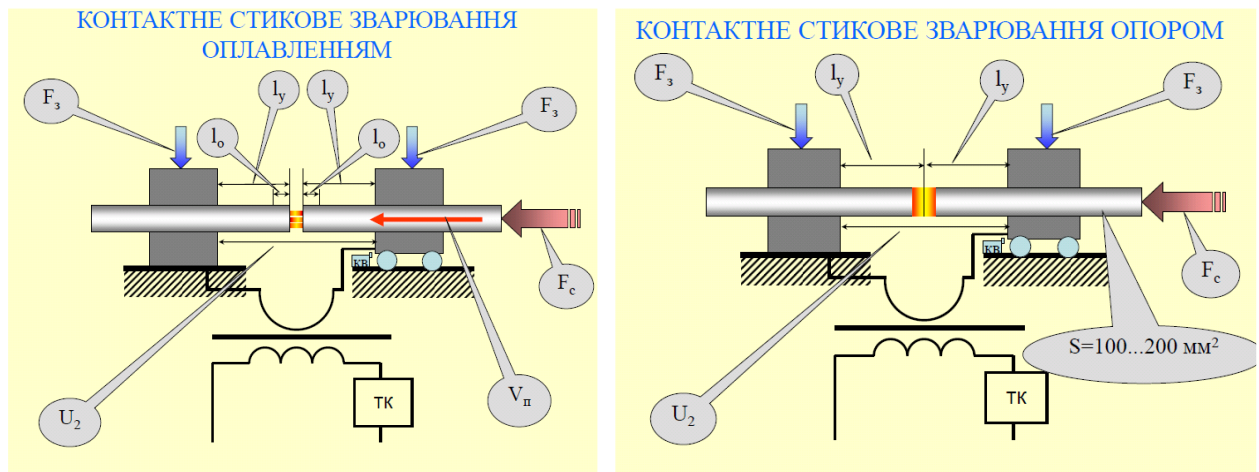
Загальна схема процесу контактного зварювання
